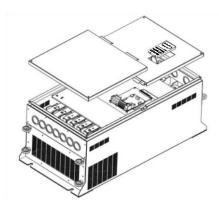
Схема демонтажа нижней крышки металлического корпуса
